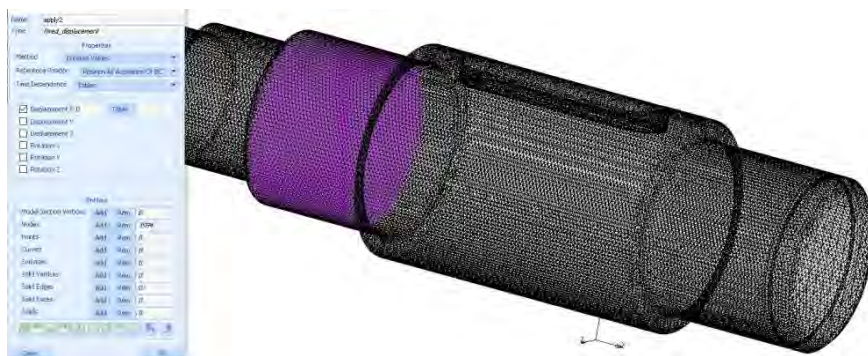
Detalle de la fijación en el apoyo B del eje de salida
